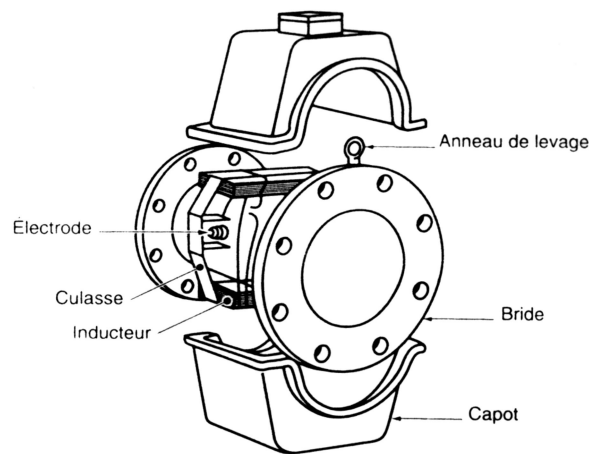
Vue éclatée d'un débitmètre à champ uniforme constant; montage à brides
